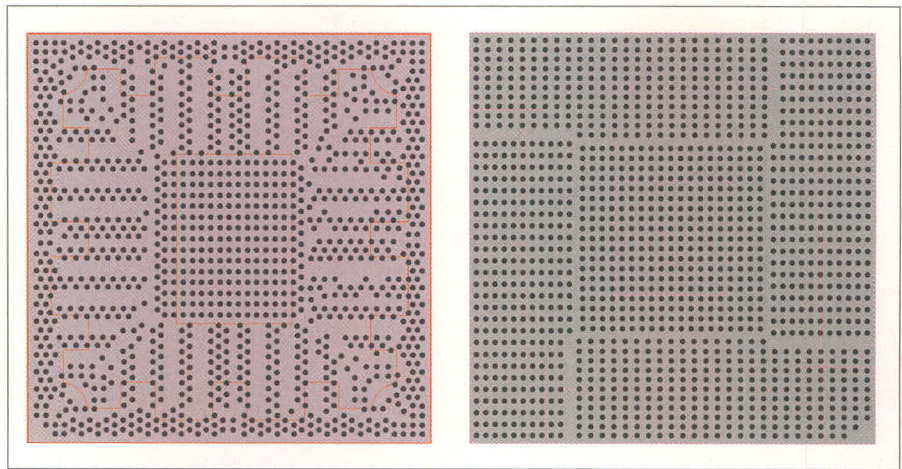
Частично регулярное расположение контактов корпуса BGA
